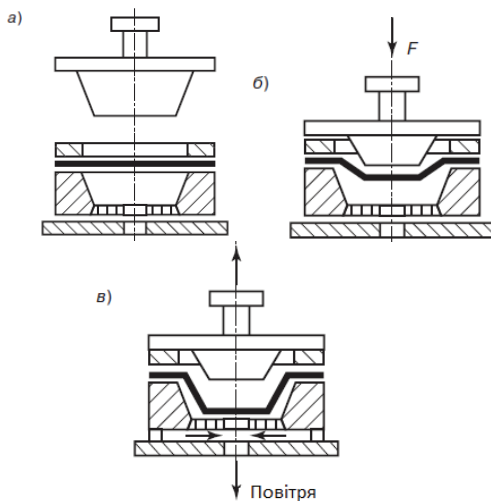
Схема негативного формування із попереднім механічним витягуванням
